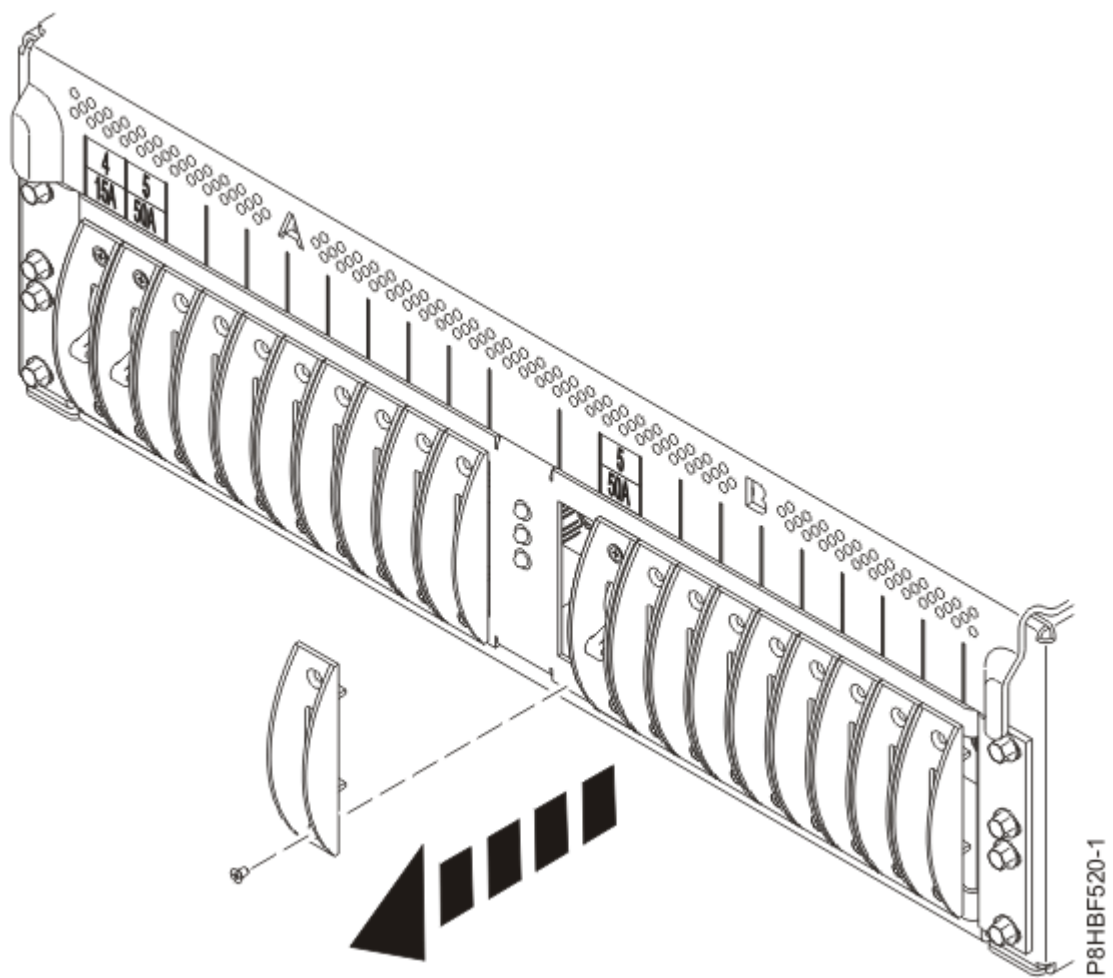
Tampa do disjuntor (a posição mostrada do disjuntor é apenas para referência)
